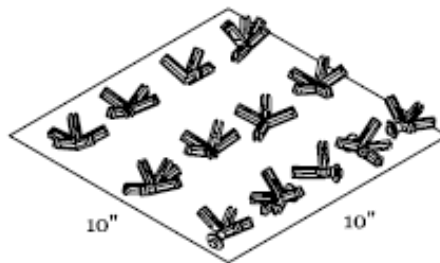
Figura I.III – Junções estruturais rebatidas no plano horizontal prontas para serem impressas na bandeja da impressora FDM. Fonte: Shea et al., 2005: 24.
